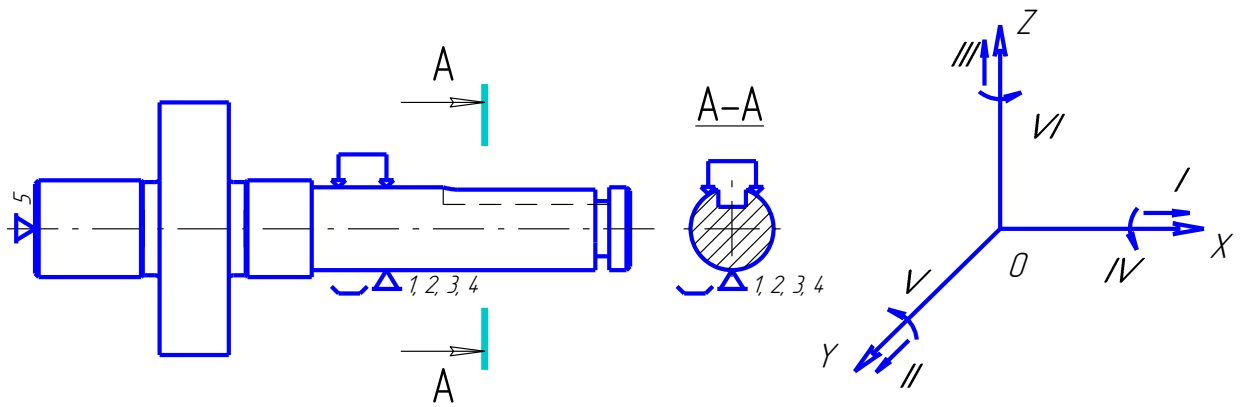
Базування заготовки на операції 050 за схемою №2
